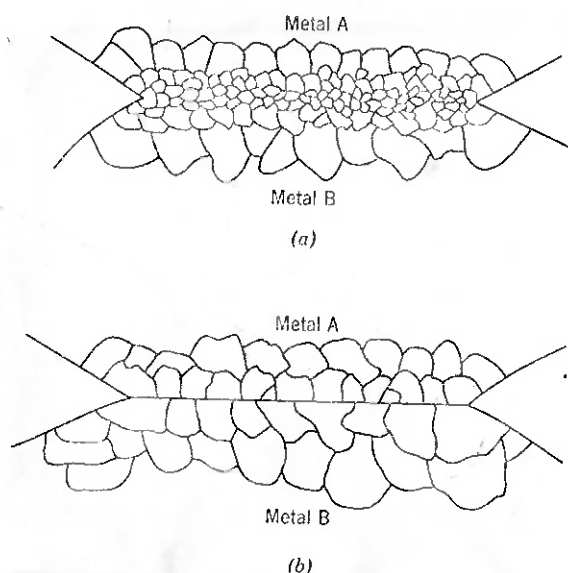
(A) Um típico weld metalúrgico. (B) Uma típica junção adesiva
